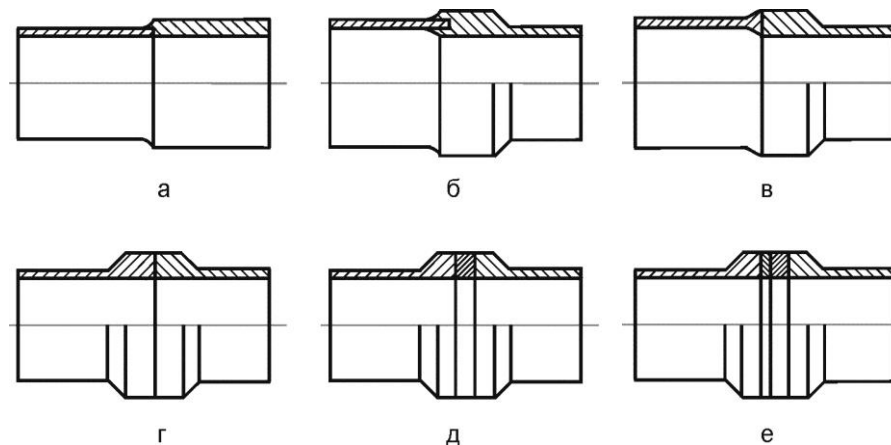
Конструкция стыков сварных соединений трубных переходников
